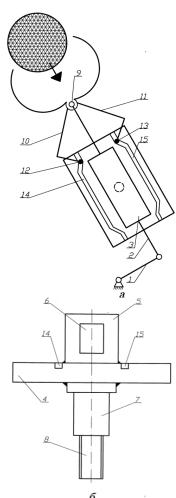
Устройство для захвата и переноса изделий [5]: *a* – кинематическая схема; *б* – стержень 3 передаточного механизма
